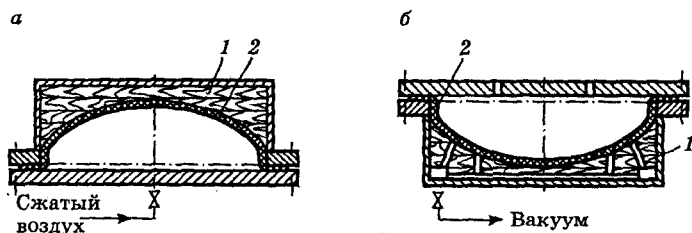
Схема пневматического (*a*) и вакуумного (*б*) прессования: 1 — матрица; 2 — изделие
